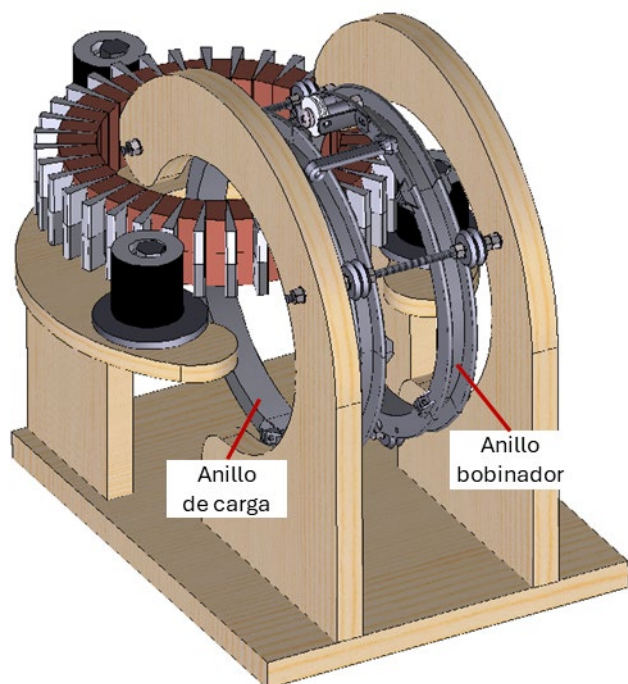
a) Diseño de la máquina bobinadora de núcleos toroidales presentada en [3], tras mejoras que le otorgan mayor robsutez.
